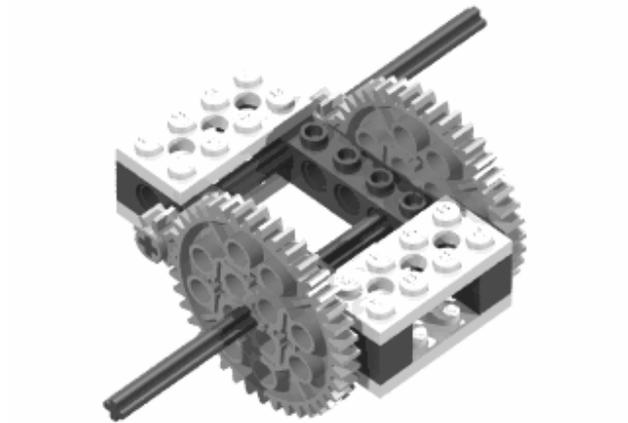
Engrenage à rattrapage de jeu à partir de pièces LEGO
